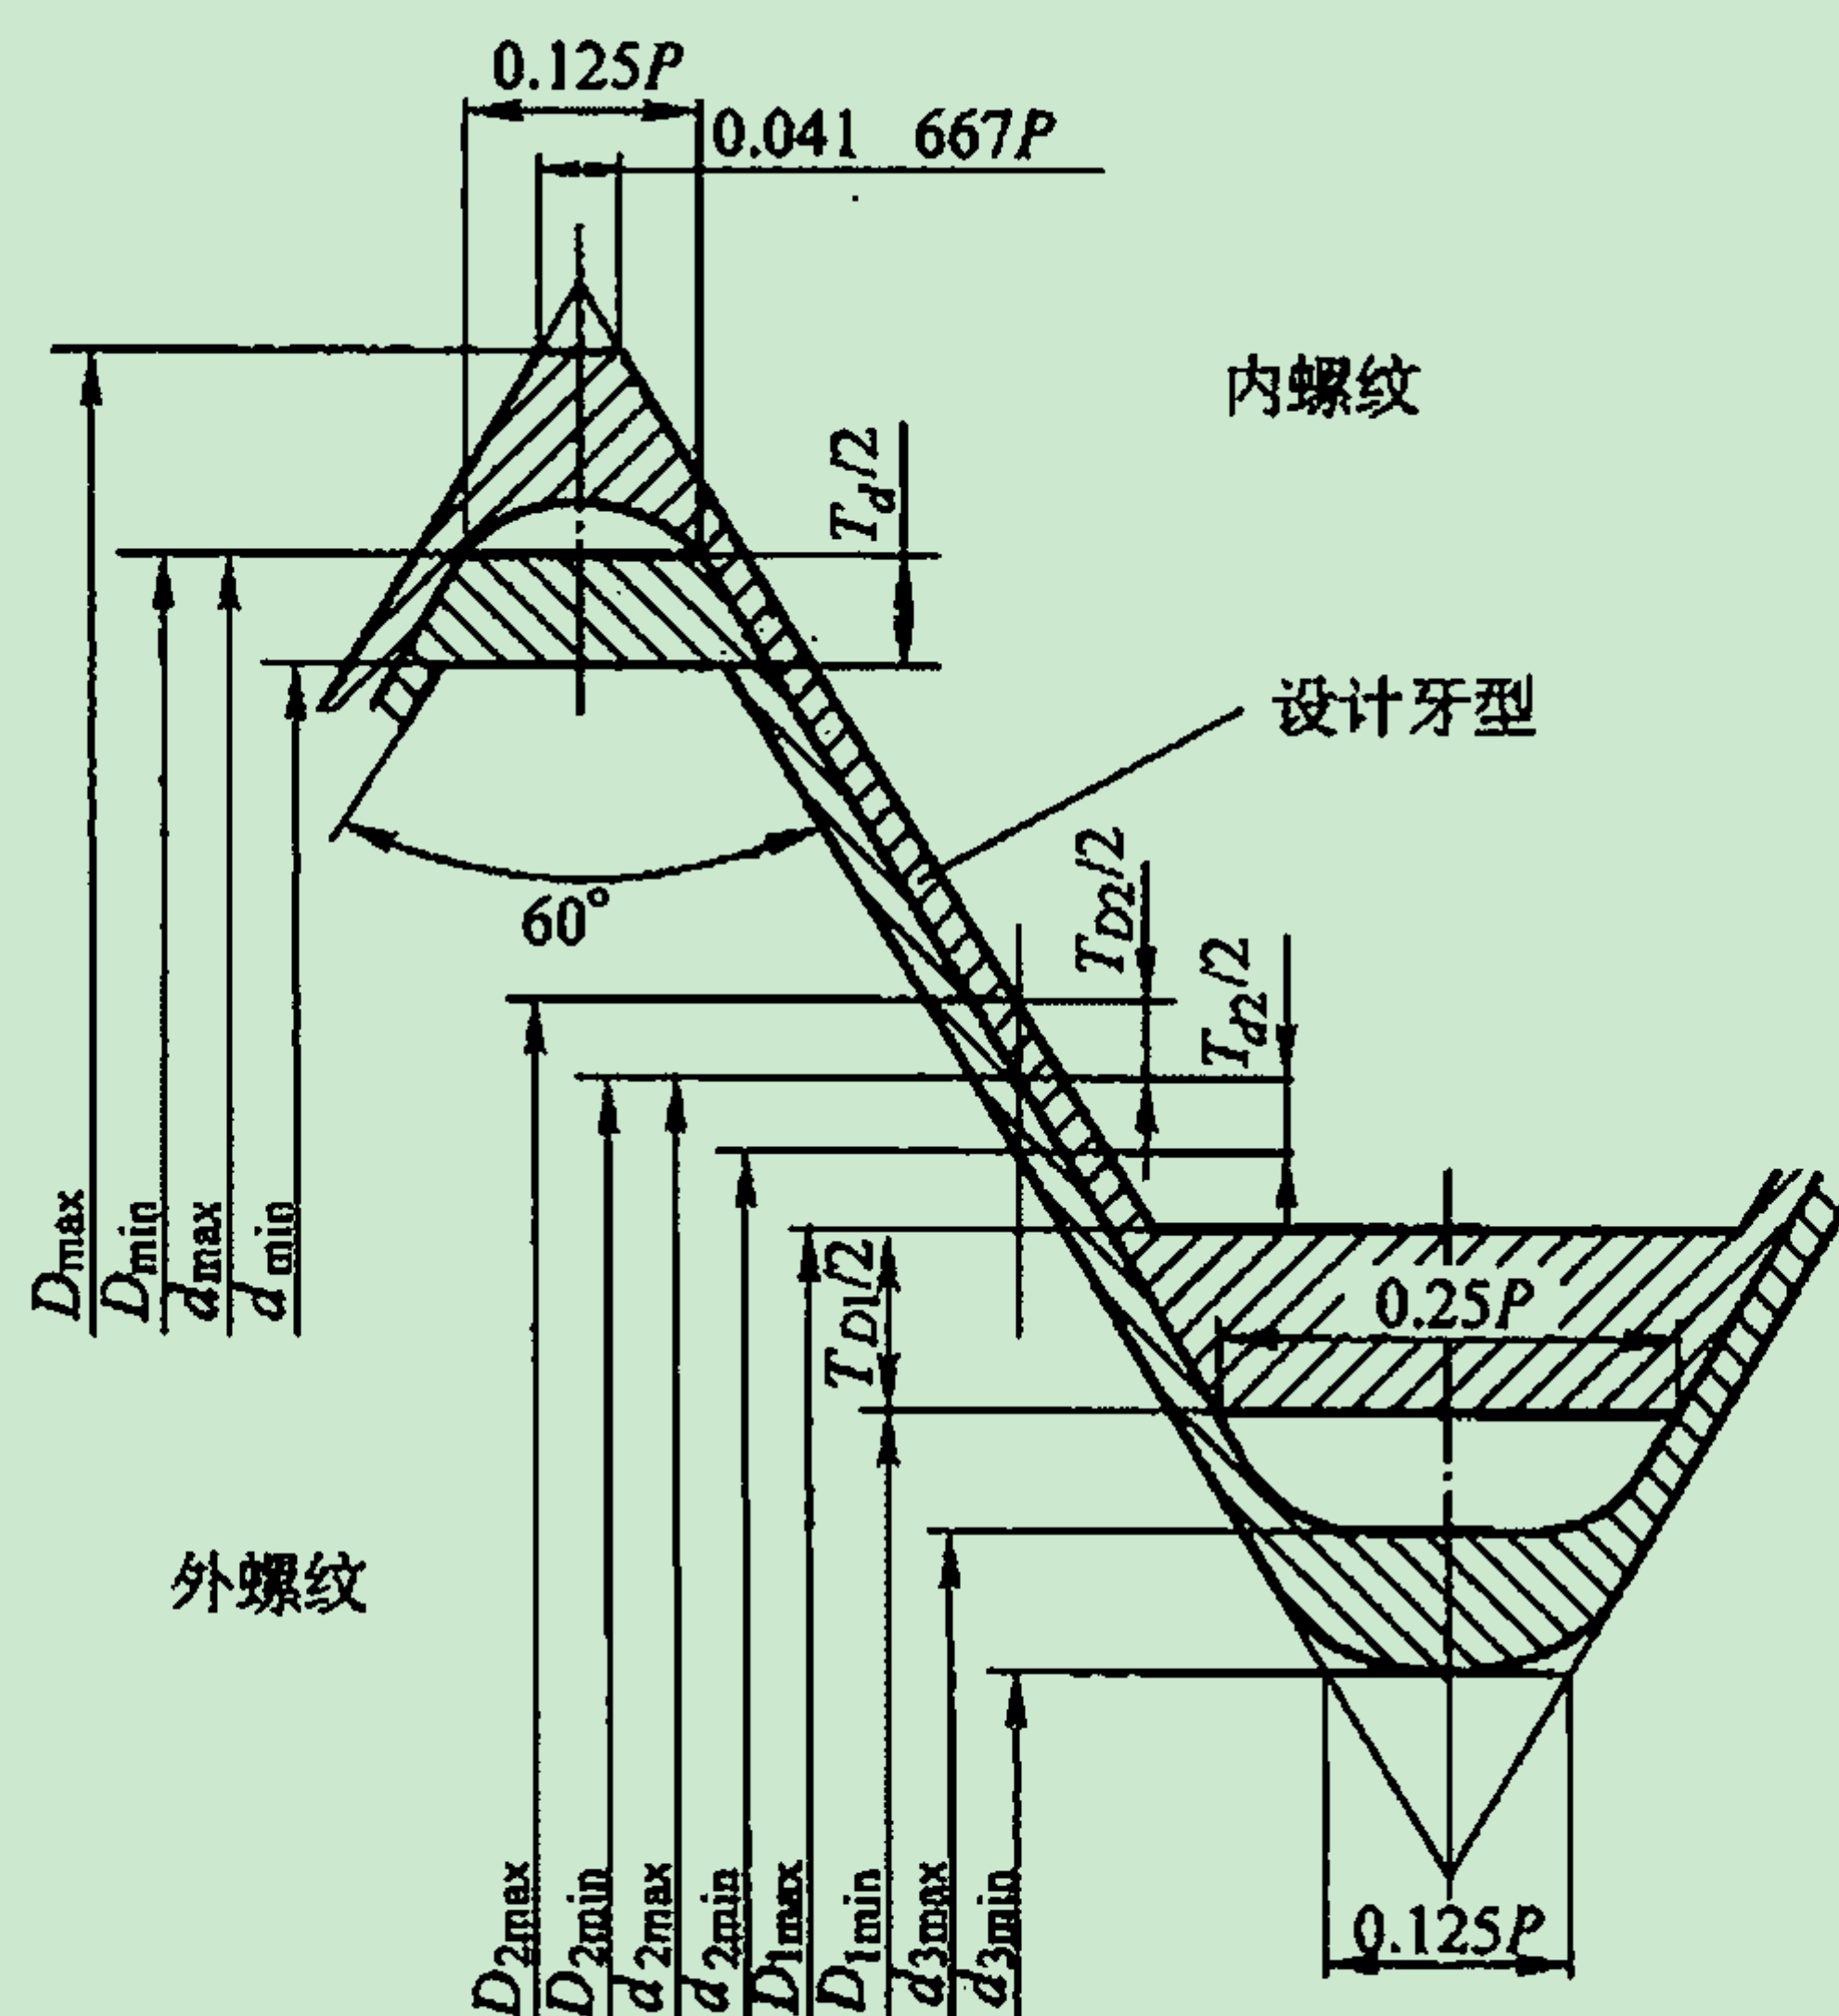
3A 和 3B 螺纹的公差带位置
